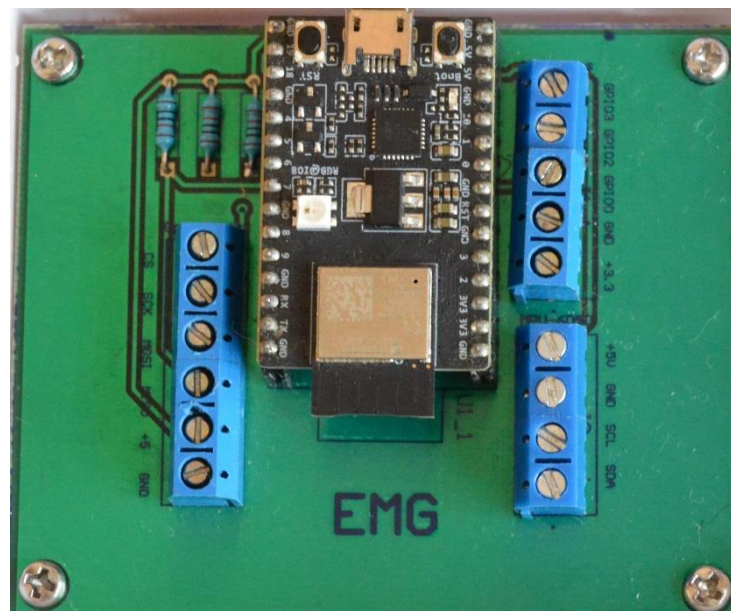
Placa PCB. Fuente: Elaboración propia.
